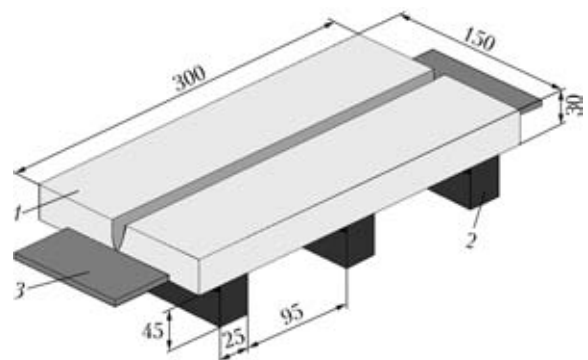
Схема жесткой пробы из стали 25Х2НМФА: 1 — пластина; 2 — ребро жесткости; 3 — выводная планка
